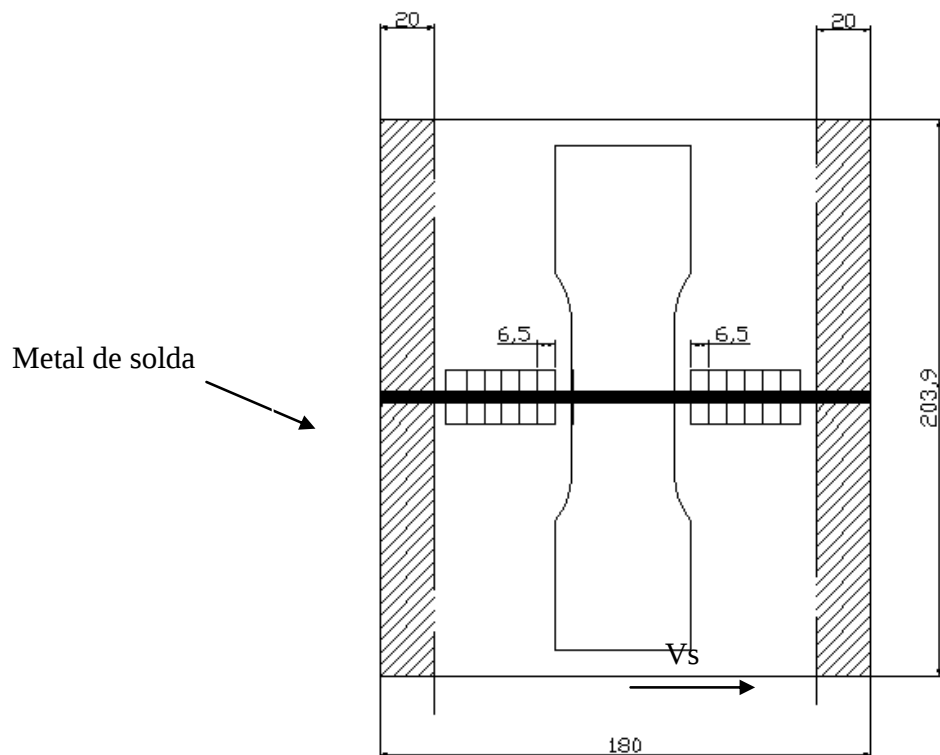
Modo de retirada do corpo-de-prova de tração em cada junta soldada.
